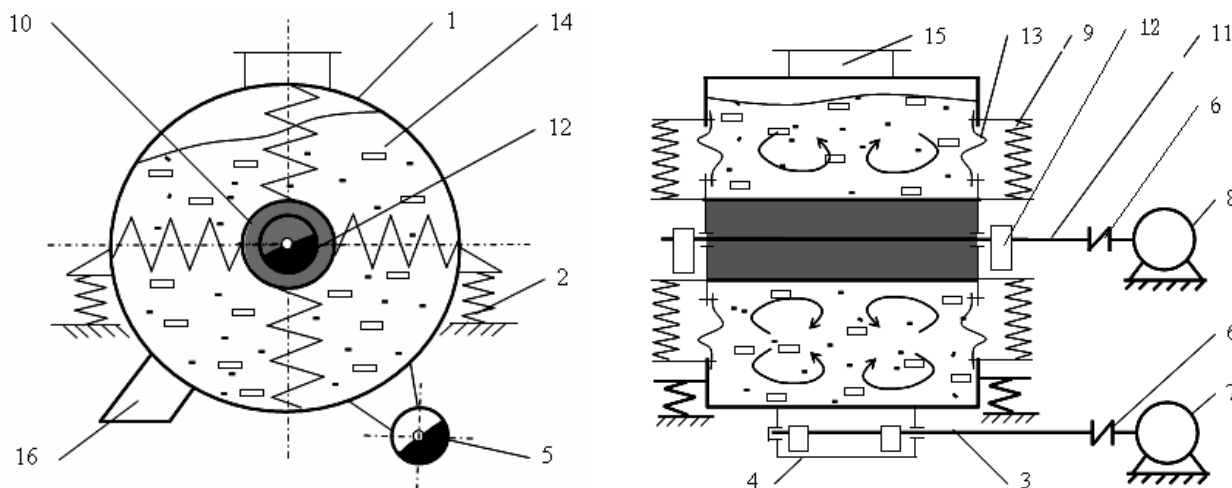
Конструктивне рішення пристрою для віброабразивної обробки деталей
